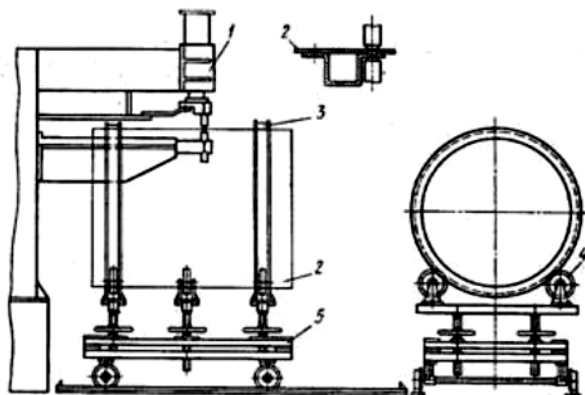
Поддерживающее приспособление для сварки крупногабаритных обечаек: 1 – машина; 2 – свариваемая деталь-обечайка; 3 – кольца; 4 – опорные ролики; 5 – тележка
